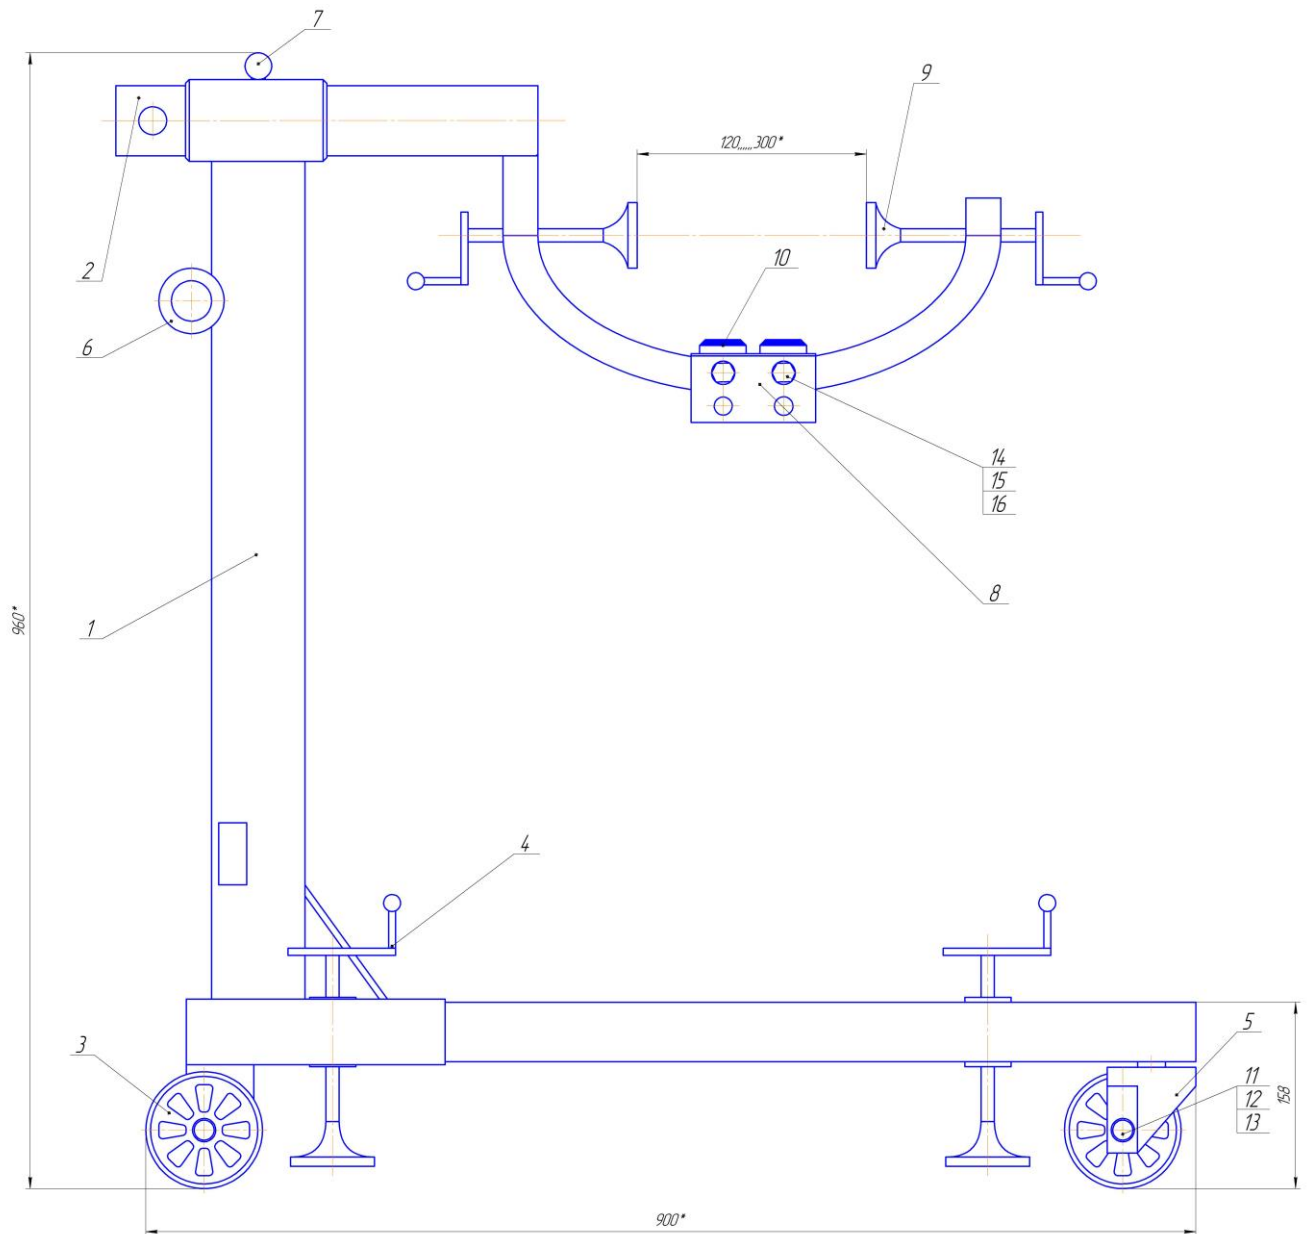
Креслення стенда для ремонту КПП:
